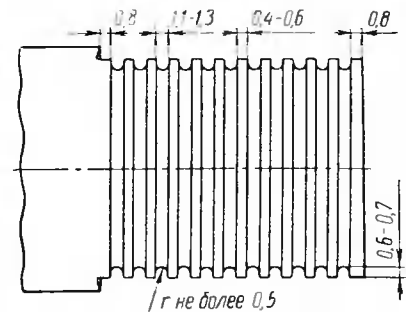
Схема подготовки цилиндрических поверхностей нарезкой кольцевых канавок
